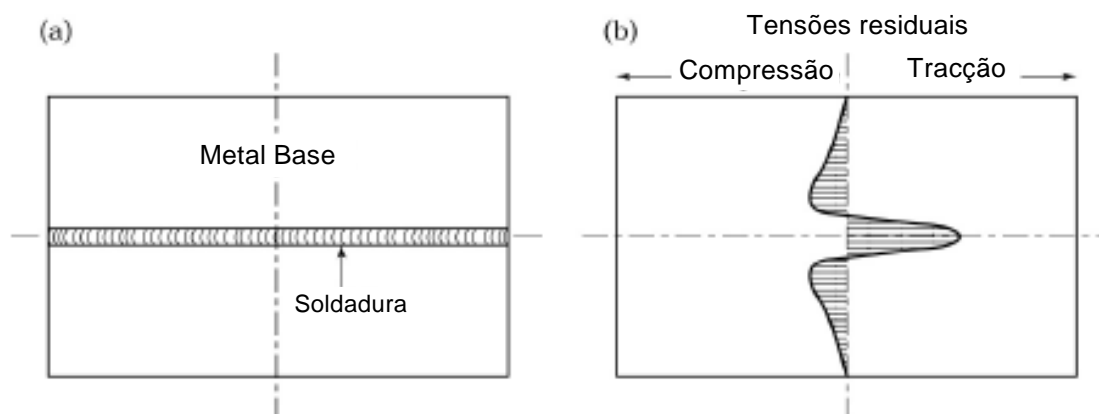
Tensões residuais desenvolvidas durante a soldadura
